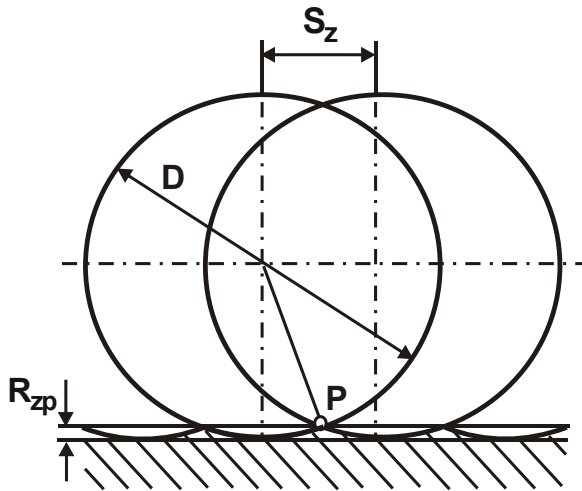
Расчетный микропрофиль обработанной поверхности при фрезеровании цилиндрической фрезой [27]
